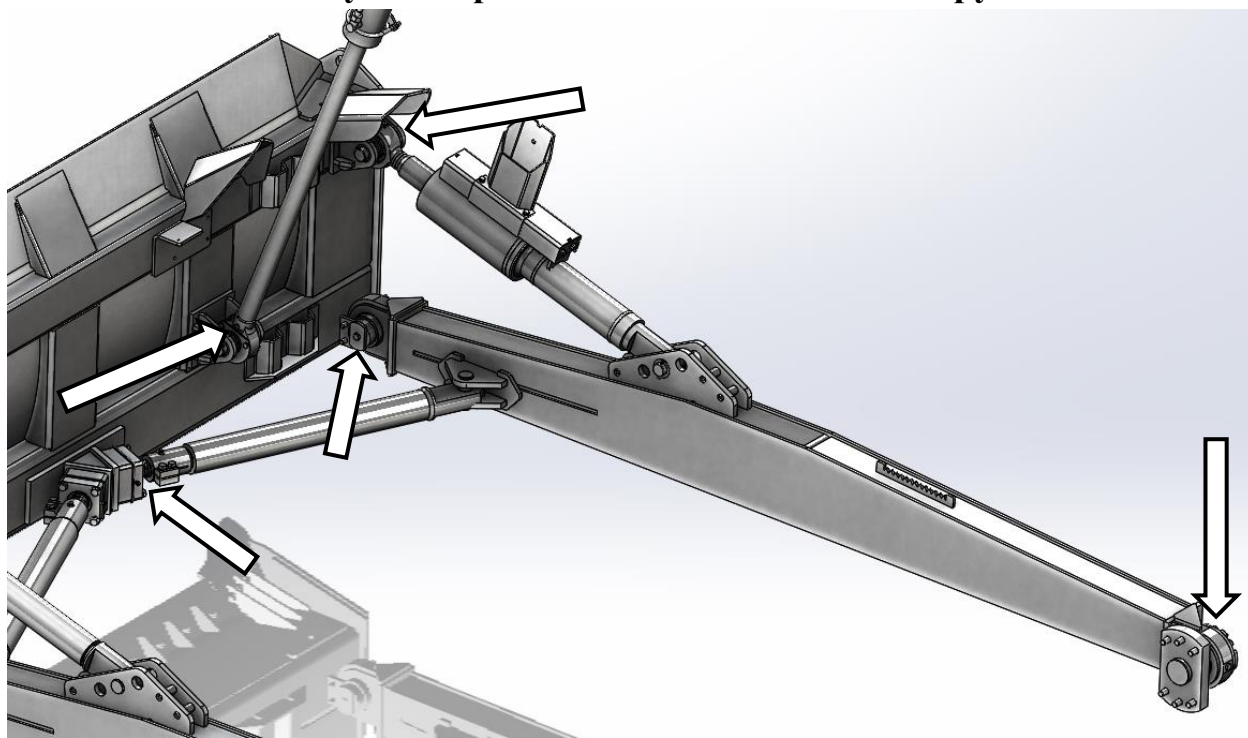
Места смазки бульдозерного отвала со съемными брусками
